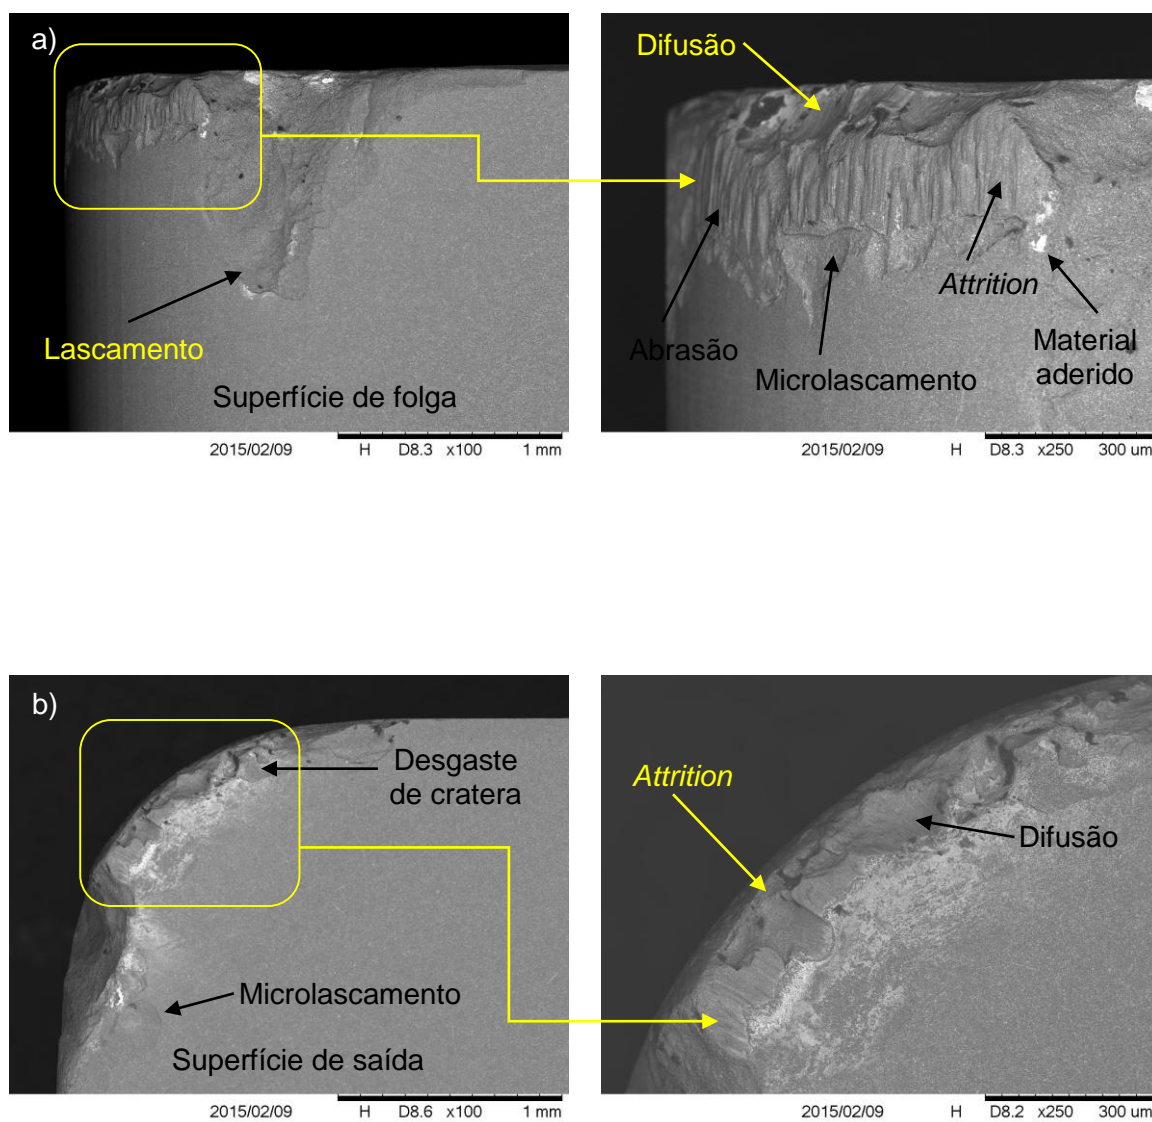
Fotografias obtidas através do MEV das ferramentas mista após a usinagem do Inconel 718 com aplicação de fluido de corte LB 2000 + 20% MoS₂ por MQF. (a) superfície de folga e (b) superfície de saída
